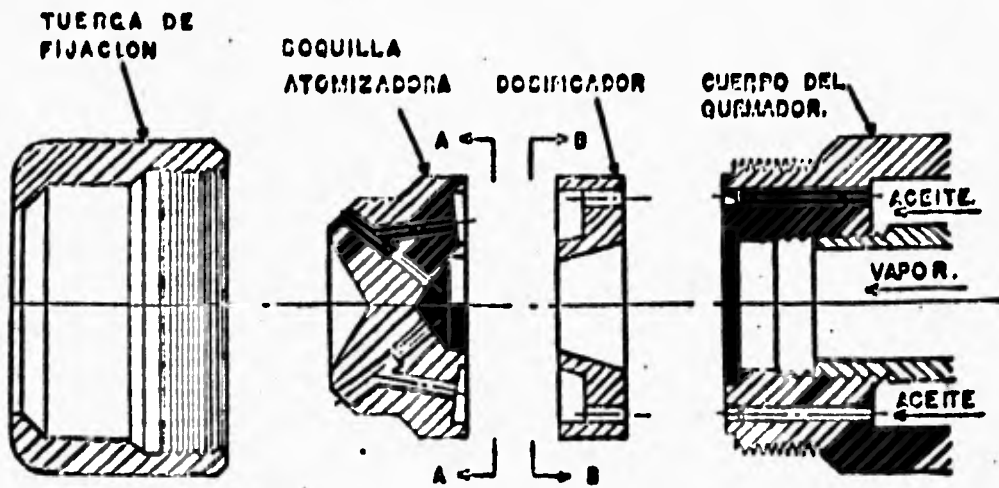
11 MONTAJE DEL CAÑON DEL QUEMADOR
